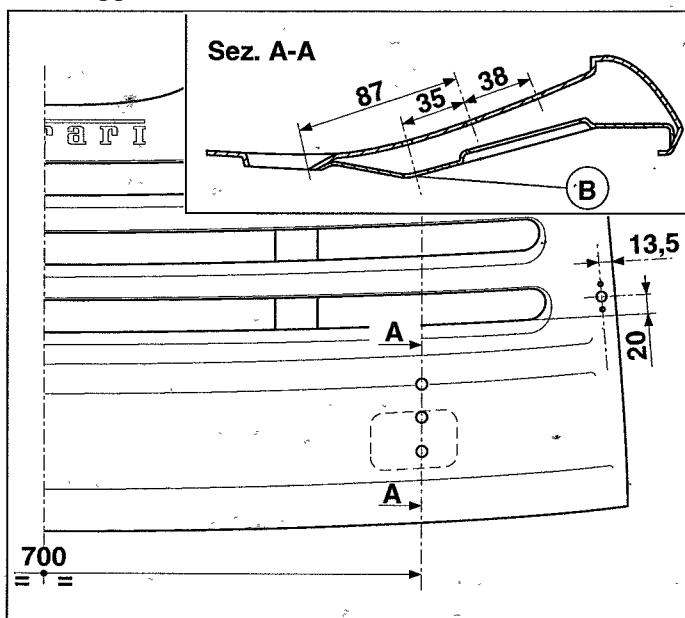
Foratura cofano motore e fissaggio tiranti
